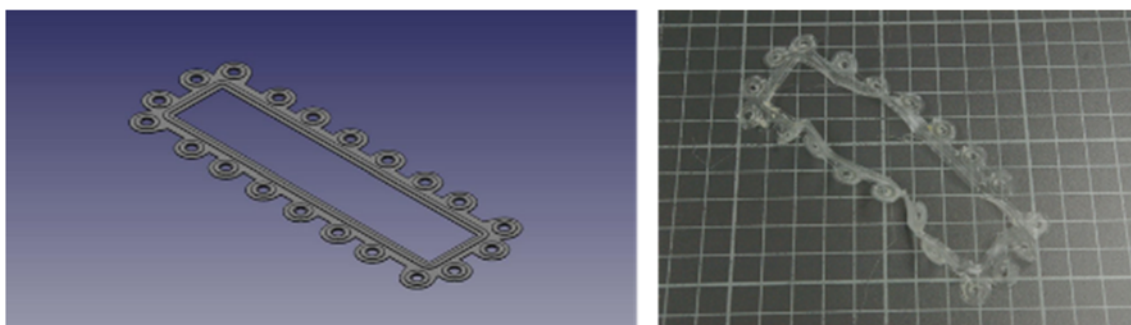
Links) CAD Modell der 3D gedruckten Flachdichtung; rechts): aus Filaflex 70A gedruckte Dichtung
